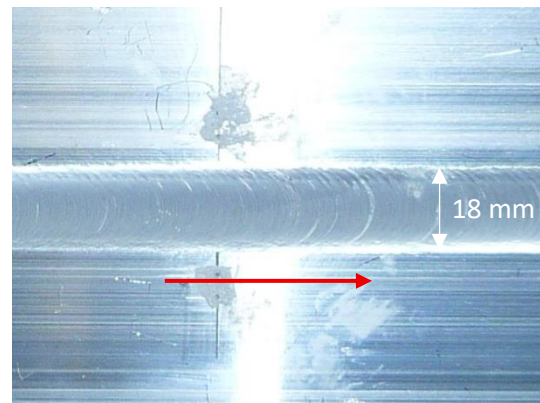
Photographie de la surface inférieure de la soudure T1 (outil B, 800 tr/min, 400 mm/min)
